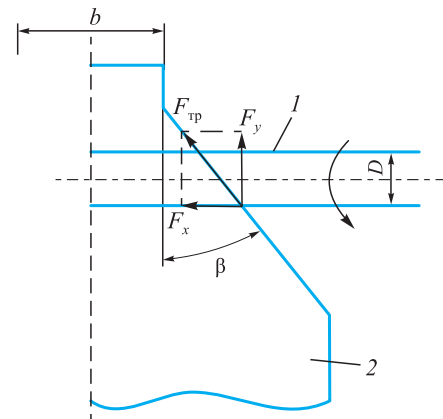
Схемы трения между цилиндрической заготовкой (1) и плоской клиновидной плитой (2) в процессе правки
